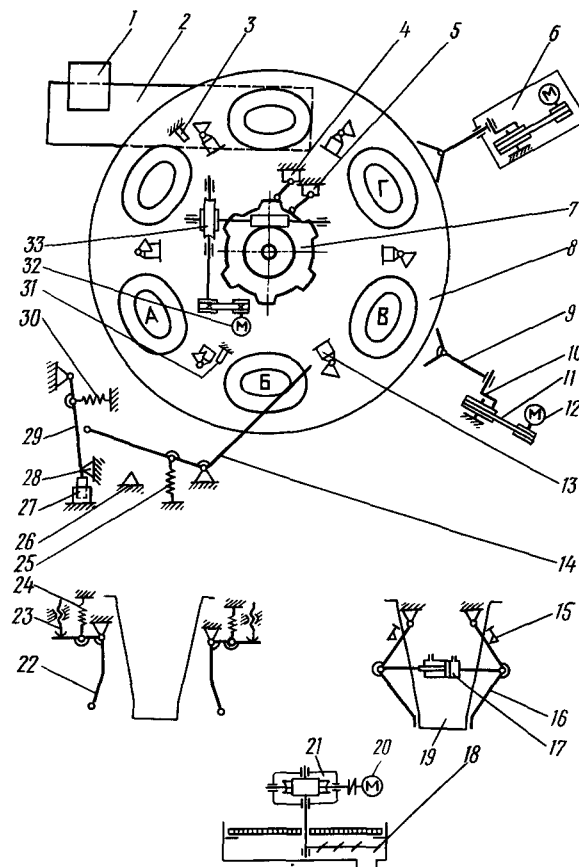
Кинематическая схема установки 6.055 АДК-50-3ВМ:
